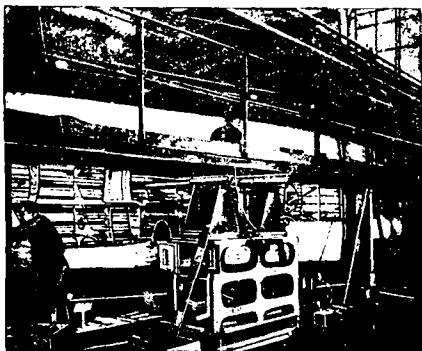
Ступели для сборки консолей крыла и центропланов имеют подвижную верхнюю балку, которая сдвигается в сторону перед подъемом из ступеля готовых агрегатов
